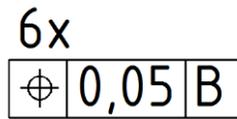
Cuadro de tolerancia para el control de varios elementos geométricos.
